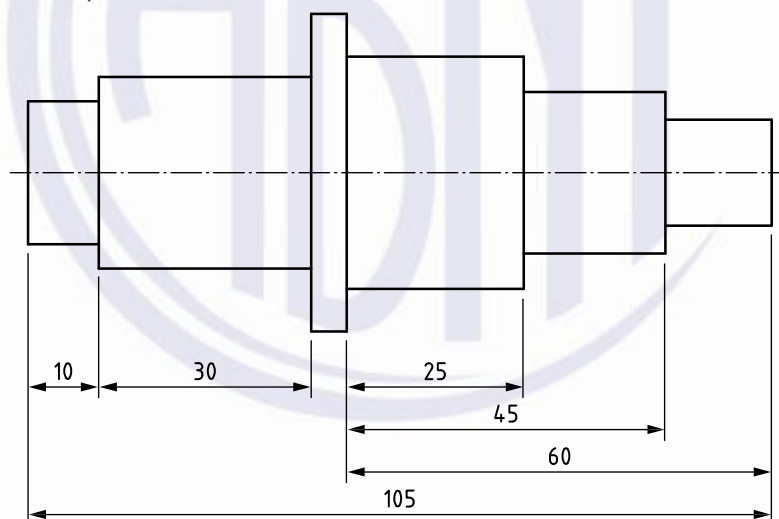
Cotagem combinada (cadeia, paralela e simples dimensões)
